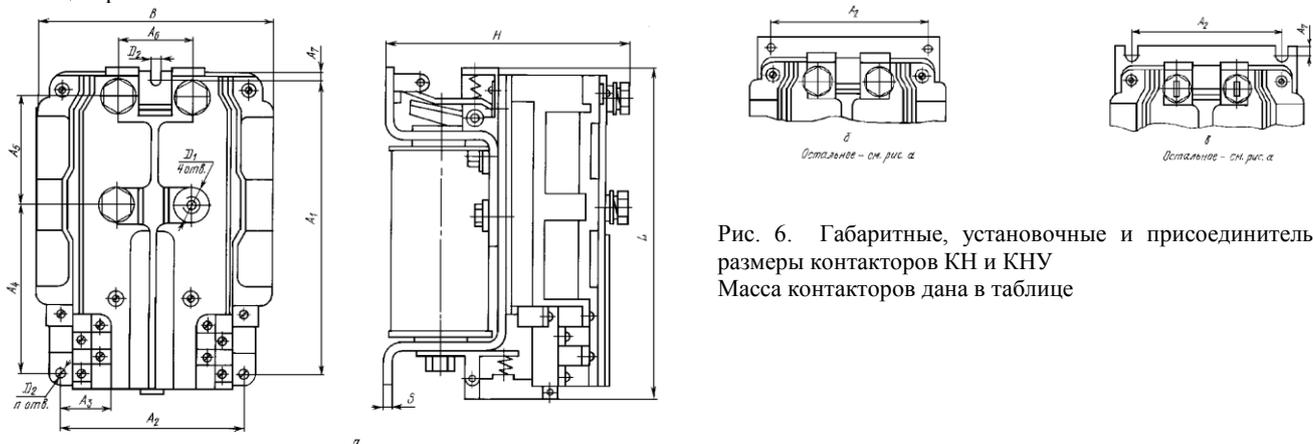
Габаритные, установочные и присоединительные размеры контакторов КН и КНУ
